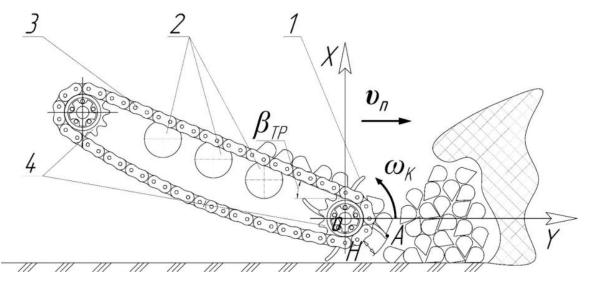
Схема к кинематическому исследованию кулачково-планчатого питателя 1 — кулачки вала; 2 — поддерживающие ролики; 3 — цепной транспортер с планками; 4 — звездочки цепного транспортера
